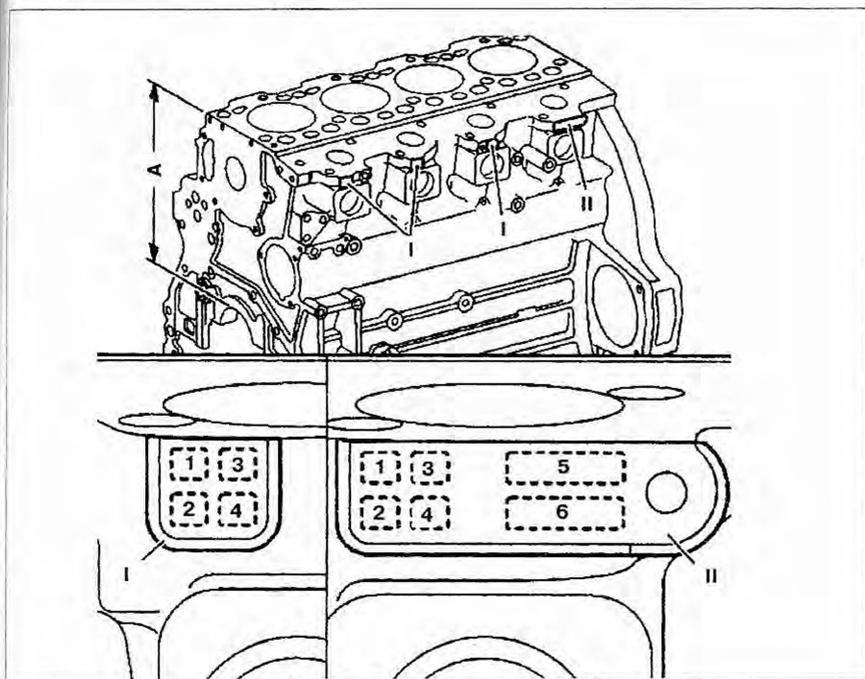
г. Маркировочные поверхности блока цилиндров.
